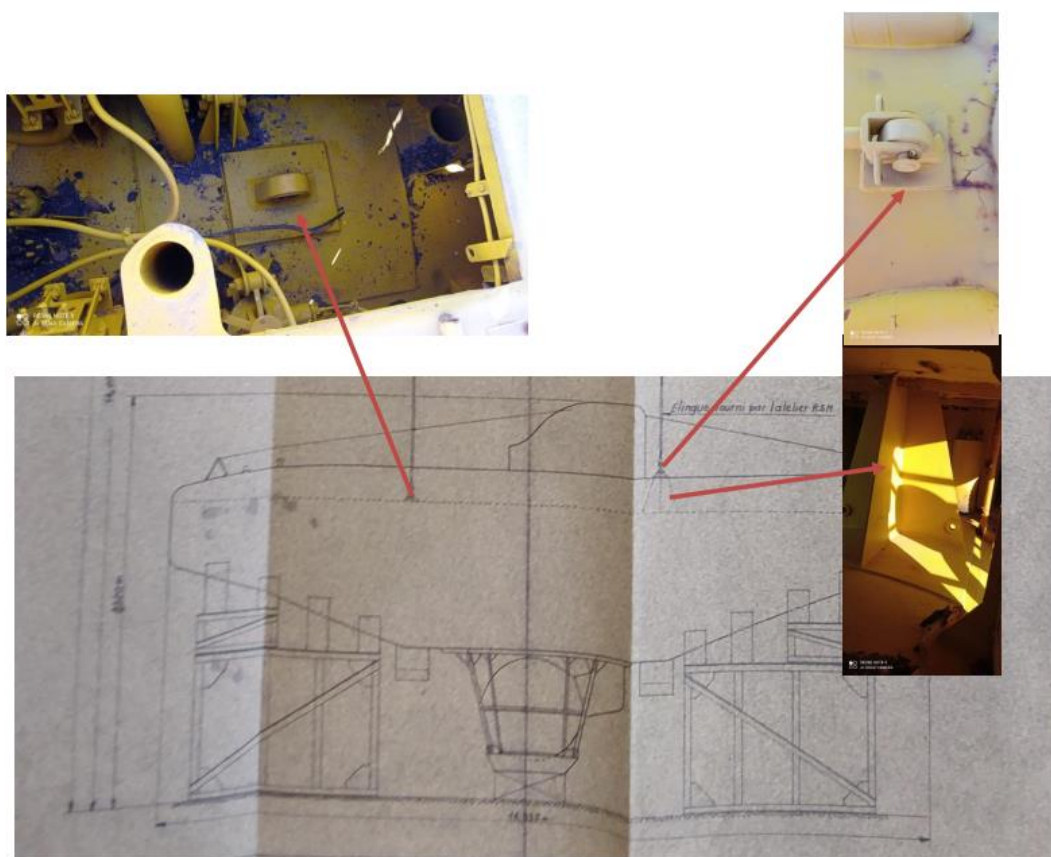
Localisation sur plan des points de levage et état des ancrages en 2025, © Breakingwave Services
